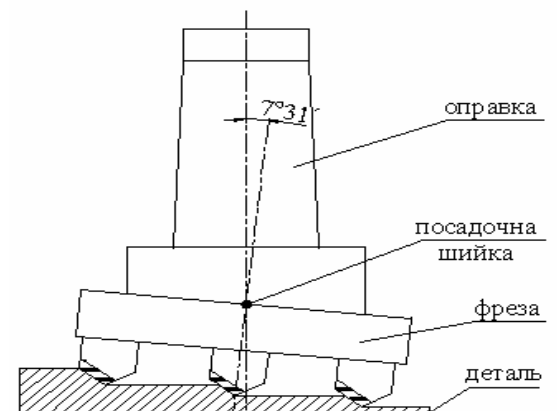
Схема прогресивного процесу фрезерування поверхні деталі
